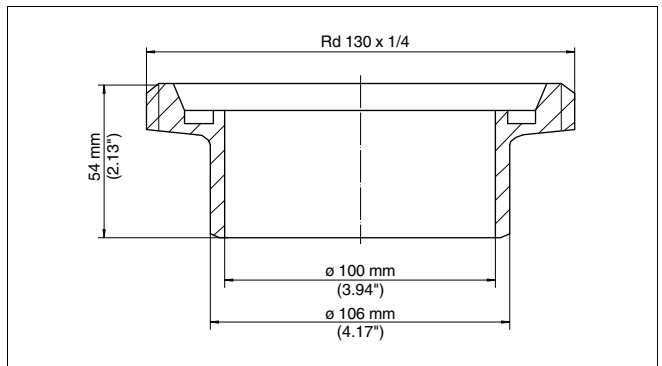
Medidas racor soldado, unión roscada según DN 100 según DIN 11851
